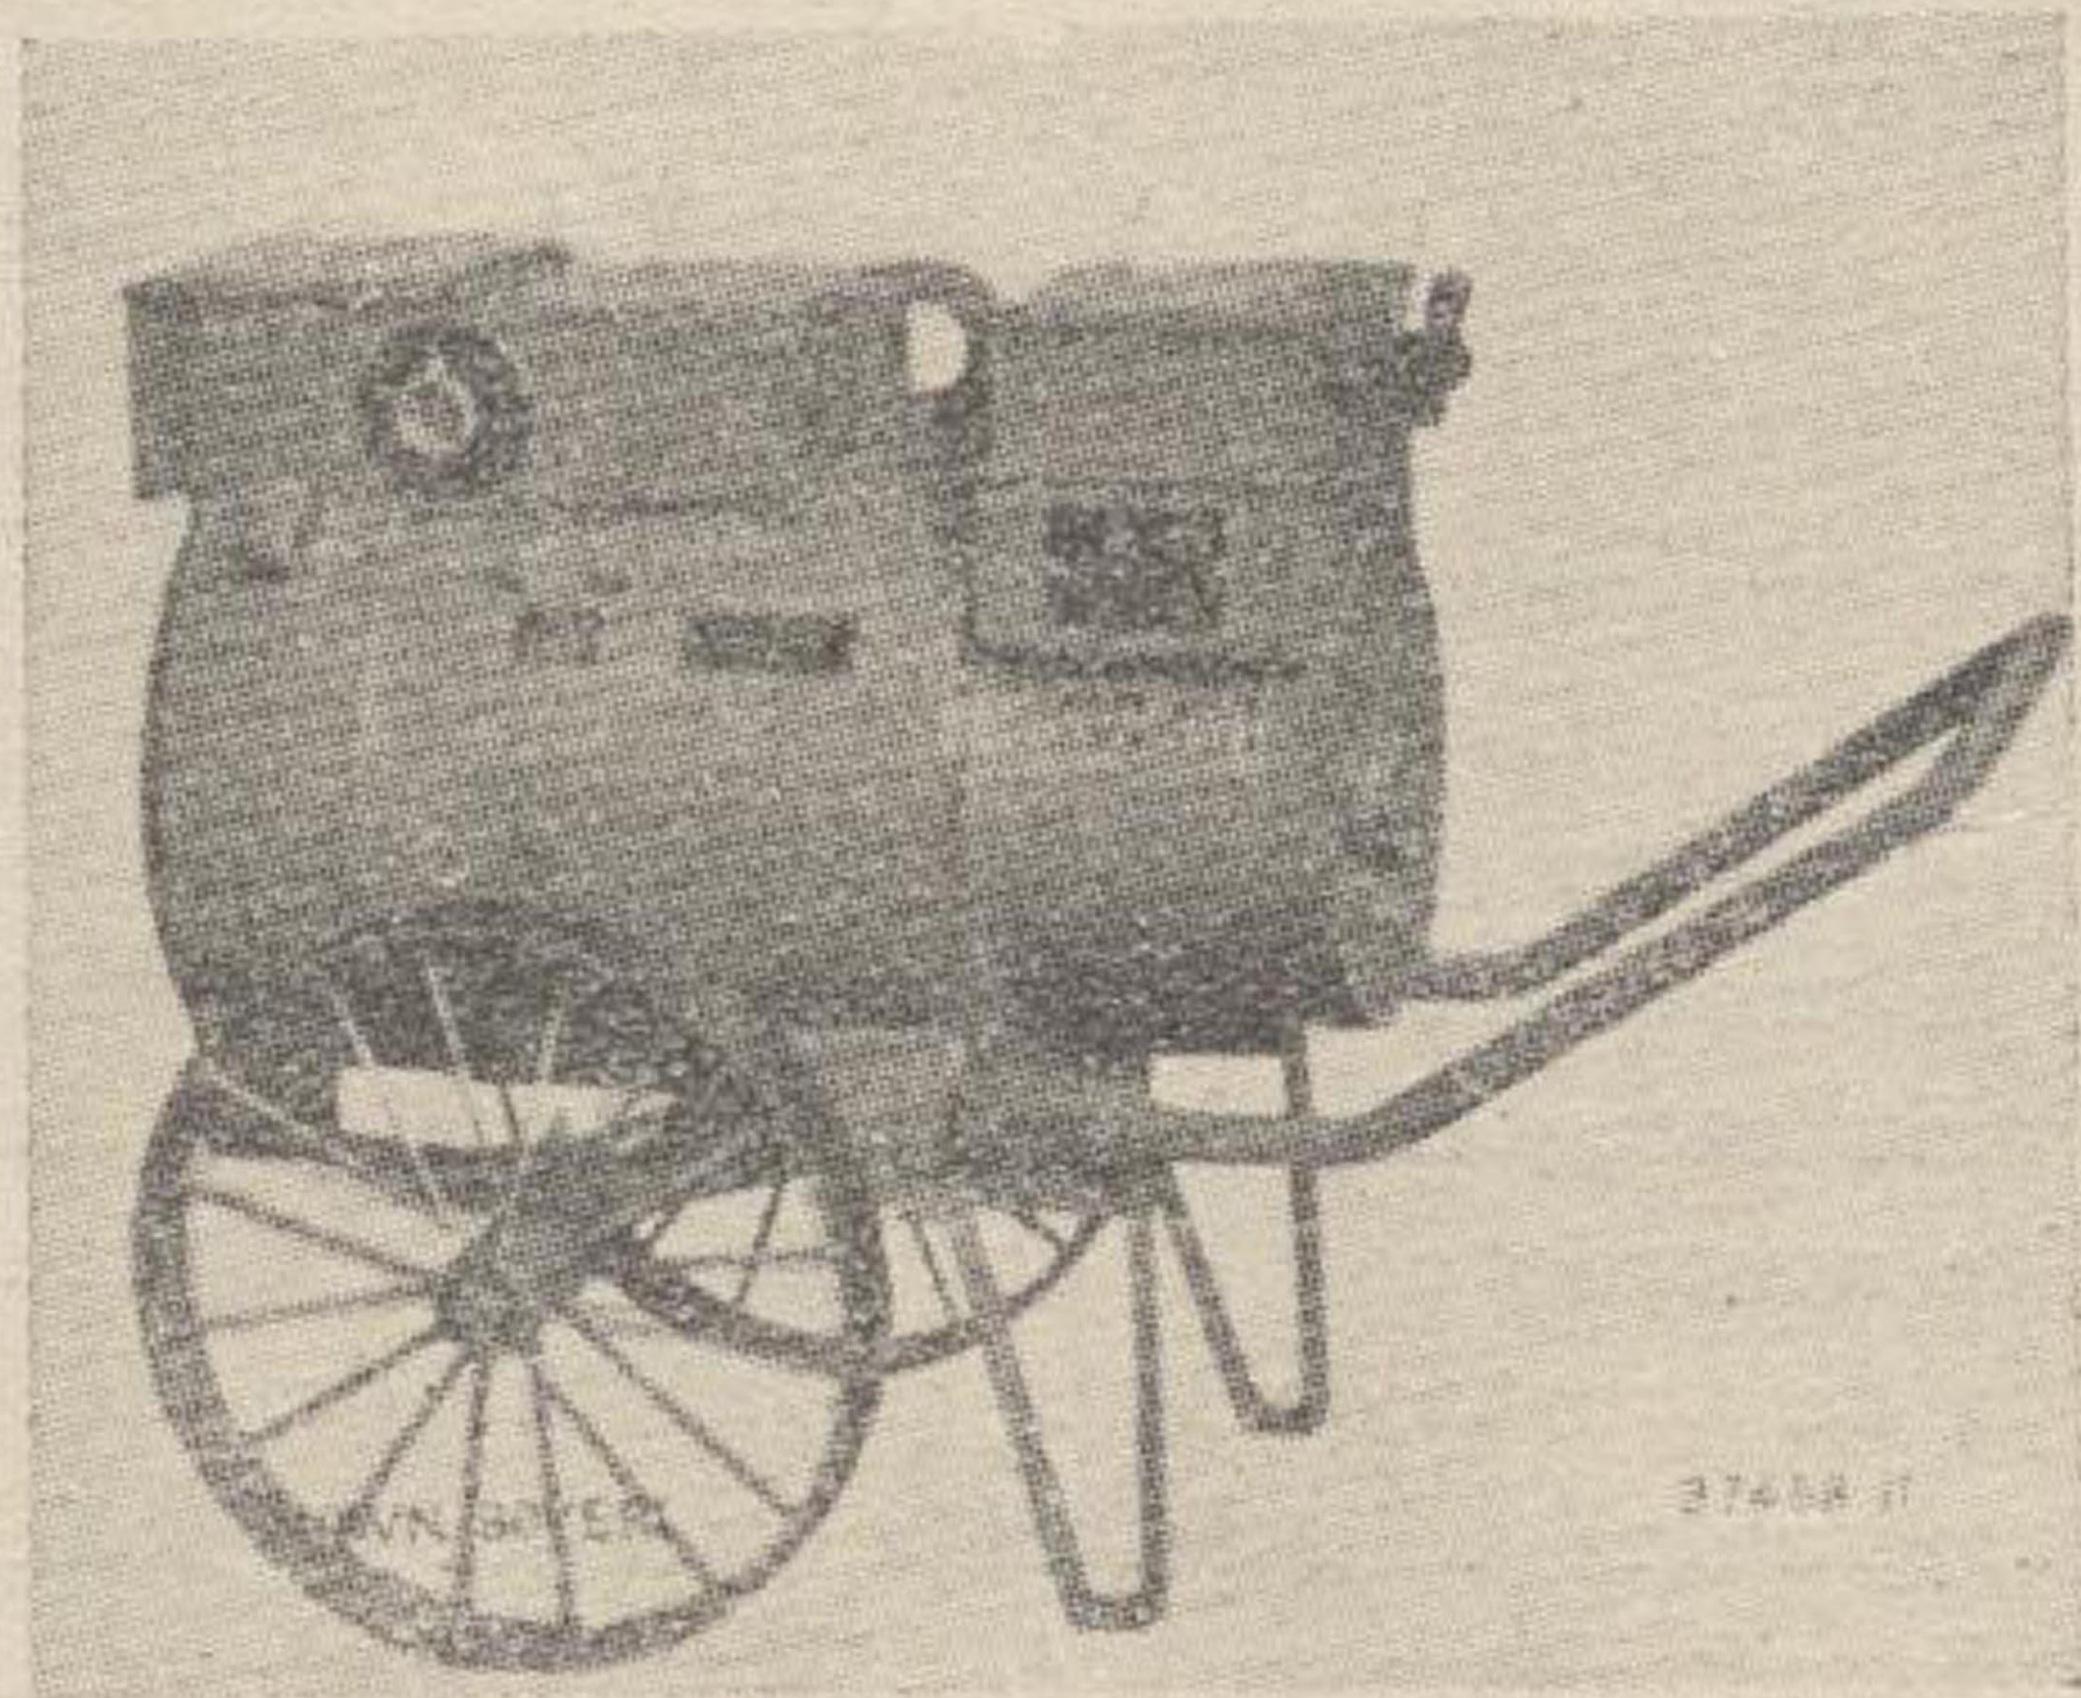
La dínamo de soldadura Brown Boveri montada en un carrito.
